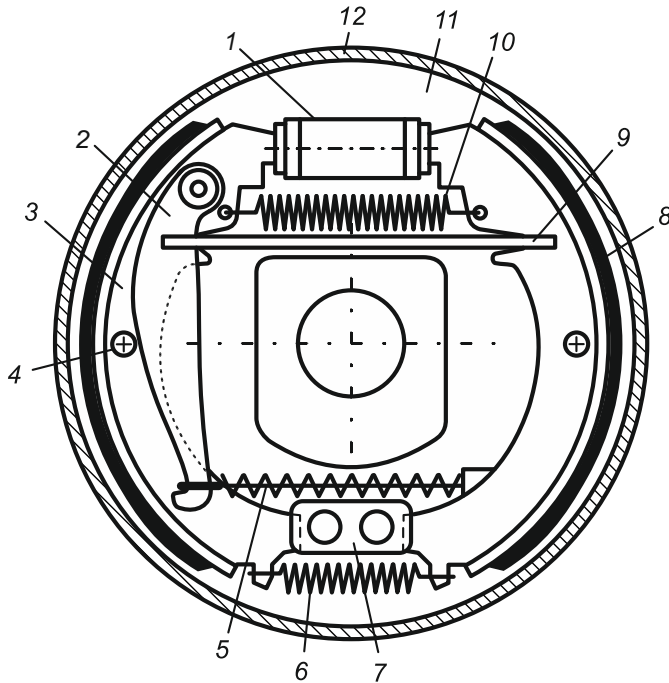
Схема колодочно-барабанного тормозного механизма заднего колеса:
